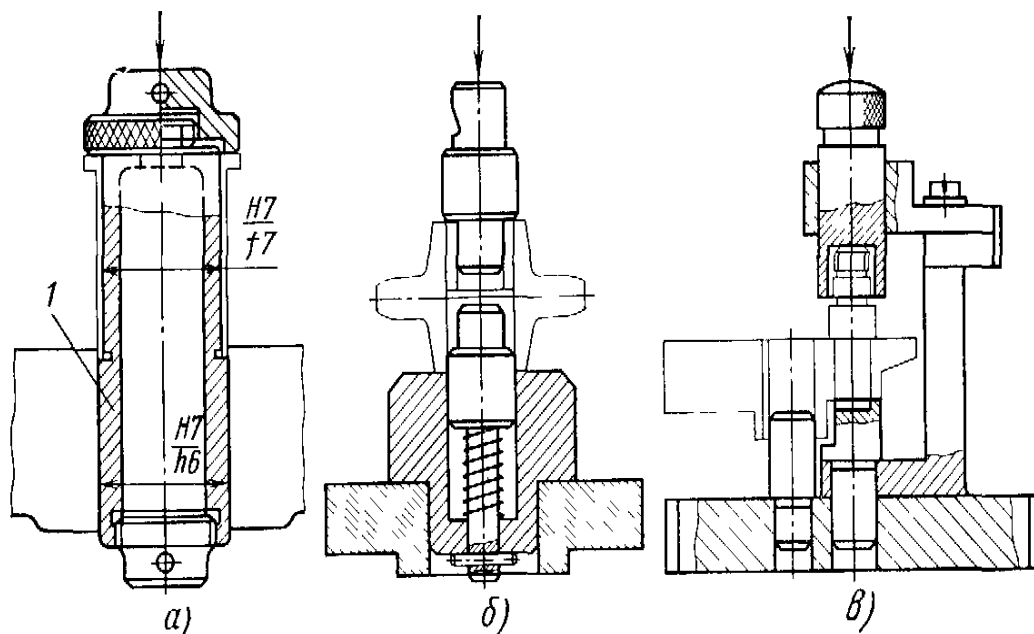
Приспособление для направления деталей при запрессовке и выпрессовке
